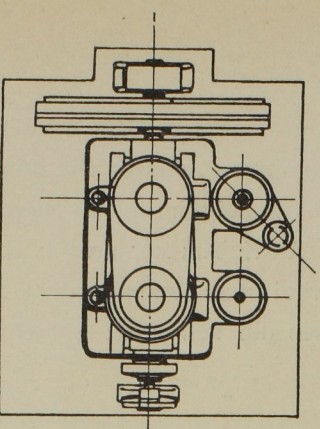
Grundriss. Massst. 1:125.
